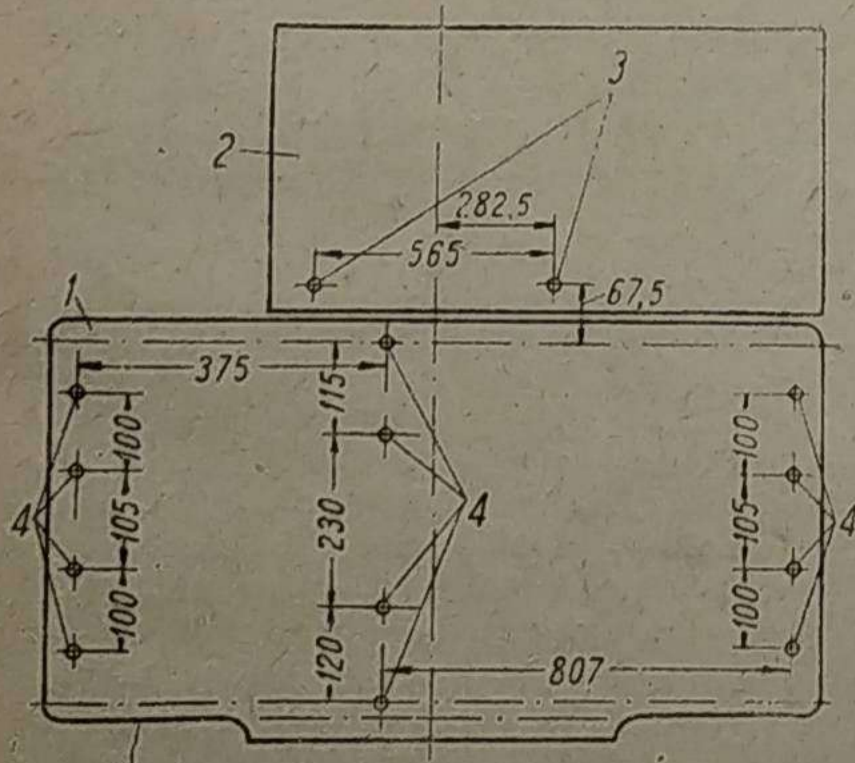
Схема расположения отверстий в корпусе заднего моста для крепления рамы газогенератора
